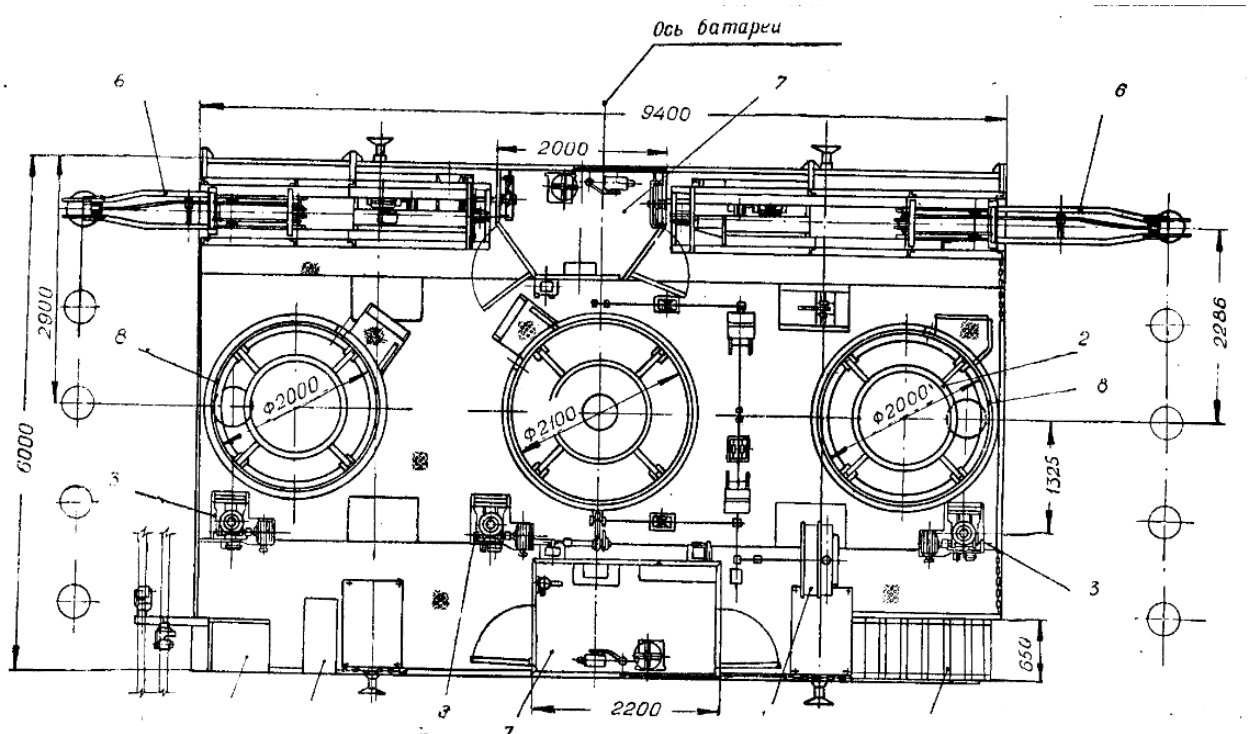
Трьохбункерний вуглезавантажувальний вагон конструкції конструкторського бюро Главмашмета. Вид зверху.
